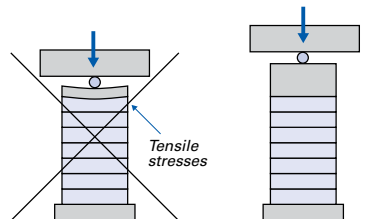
Richtiges Dimensionieren der Endstücke bei punktförmigem Kontakt
